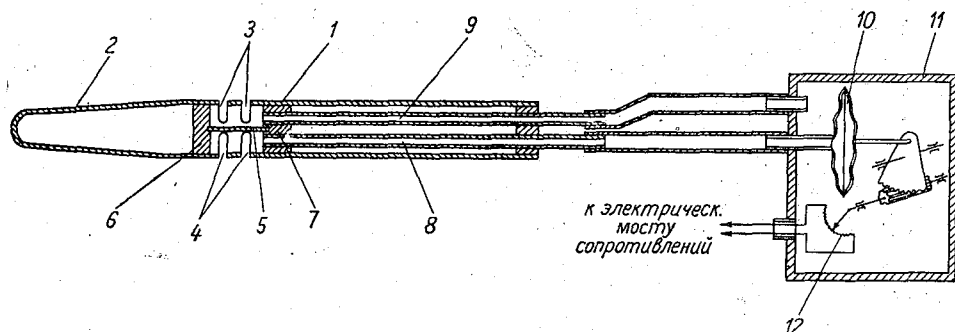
Приемник воздушного давления измерителя вертикальных потоков (ИВП). 1 — трубка, 2 — наконечник, 3, 4 — статические щели, 5 — перегородка, 6, 7, — торцевые заглушки, 8, 9 — штуцера, 10 — манометрическая коробка, 11 — пластмассовый герметический корпус, 12 — потенциометр.
